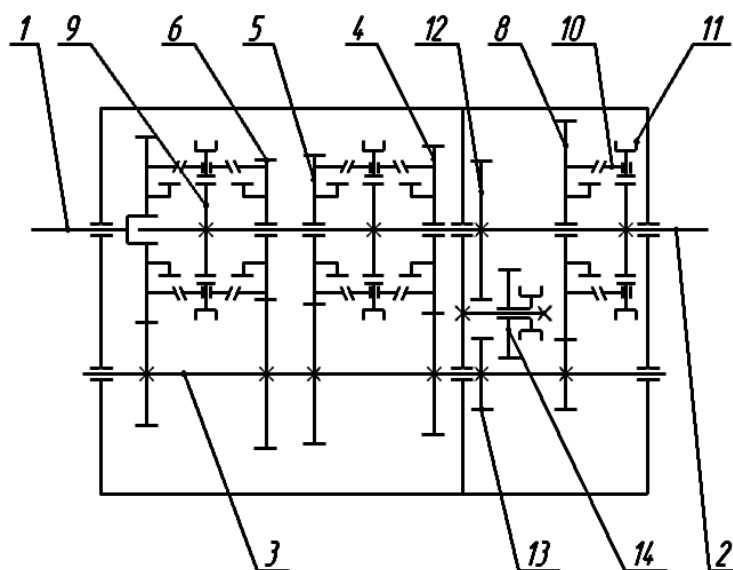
Кинематическая схема трехвальной коробки перемены передач:
